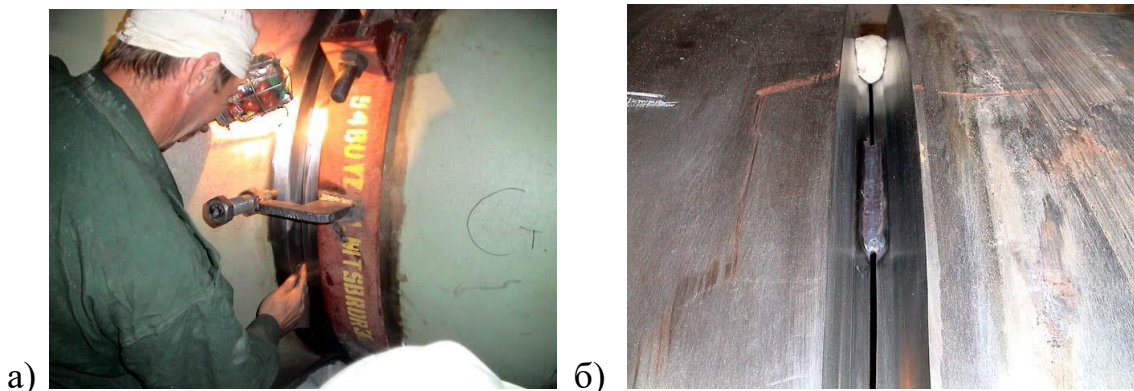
Сборка труб под сварку (а) и выполнение прихваток
